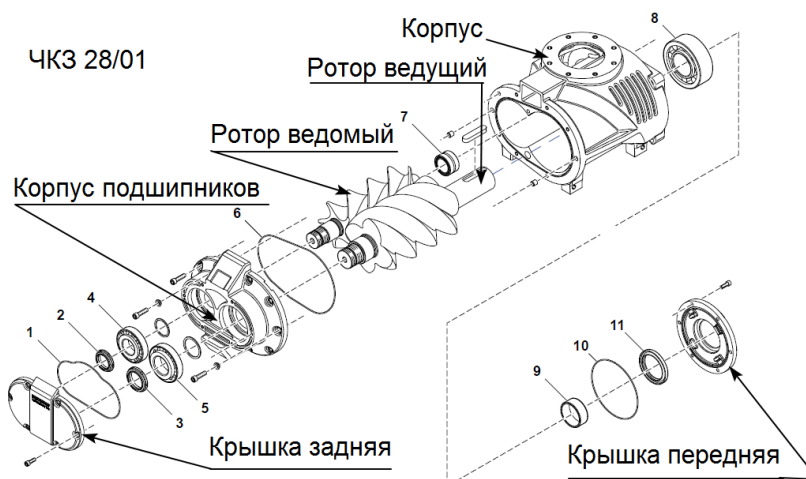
Устройство винтового компрессора ЧКЗ 28/01: 1 – кольцо 230x3,0; 2 – гайка GM 55x2; 3 – гайка–GM 65x2; 4 – подшипник 55x120x31,5; 5 – подшипник 65x130x37; 6 – кольцо уплотнительное 300x3,0; 7 – подшипник 50x72x40; 8 – подшипник роликовый 80x170x58; 9 – втулка D80xD90x35; 10 – кольцо 207x3,0; 11 – манжета 90x120x12.
